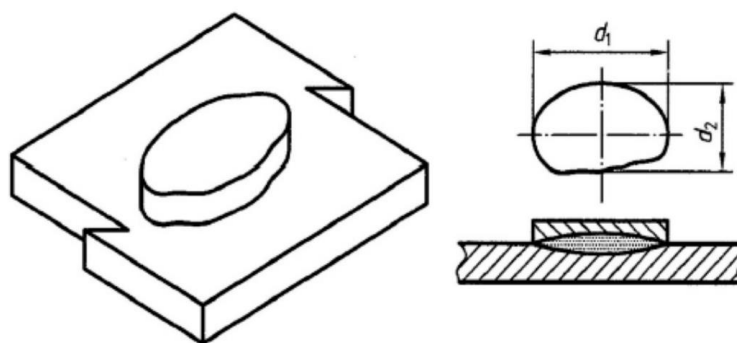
Método de medição dos diâmetros de soldadura após o ensaio destrutivo de arrancamento [39].
